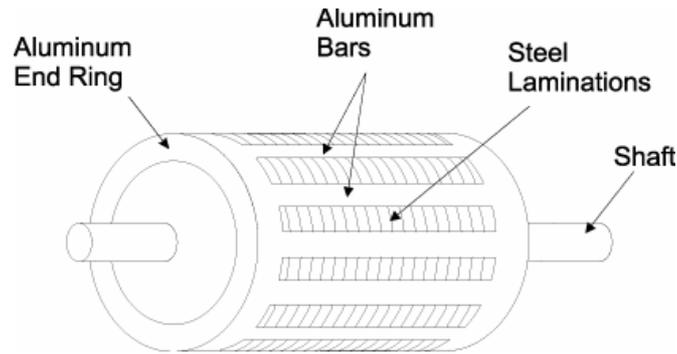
Construcción de un rotor del motor de inducción de la C A.
